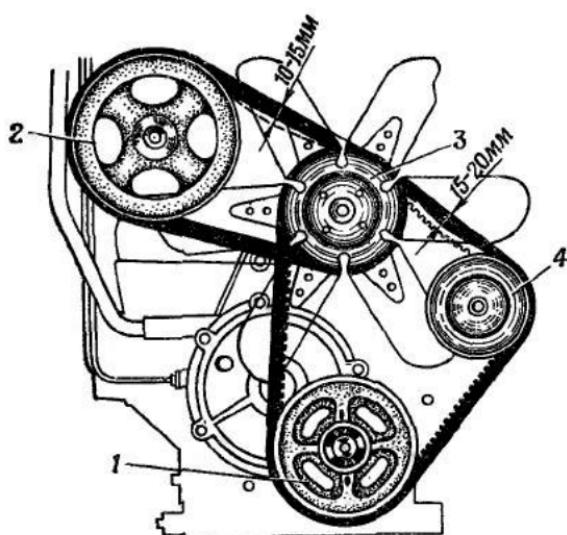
Схема натяжения ремней привода вентилятора генератора и компрессора:
